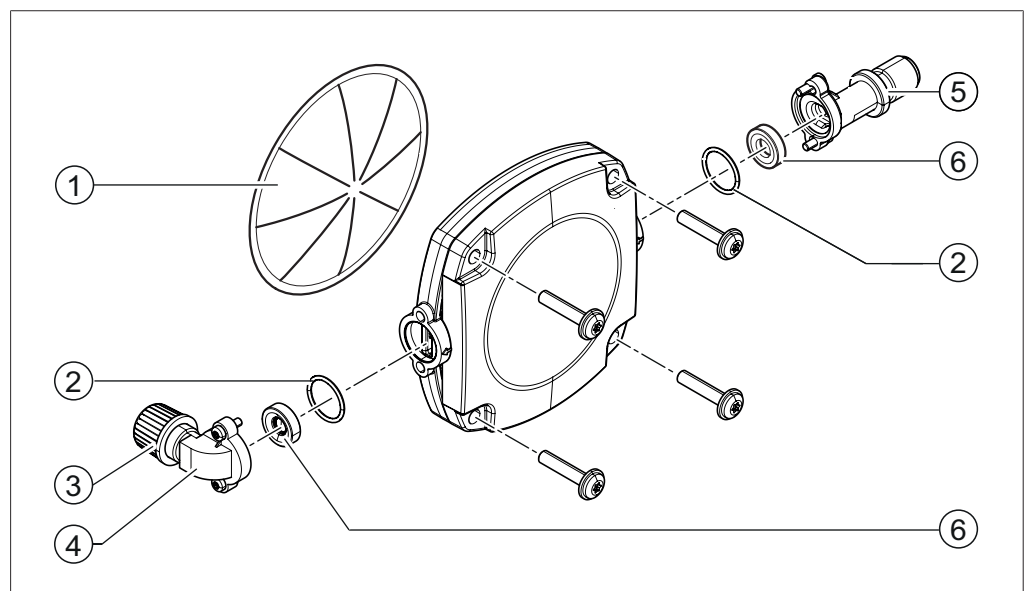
Ansicht des kompletten zerlegten Pumpenkopfs
